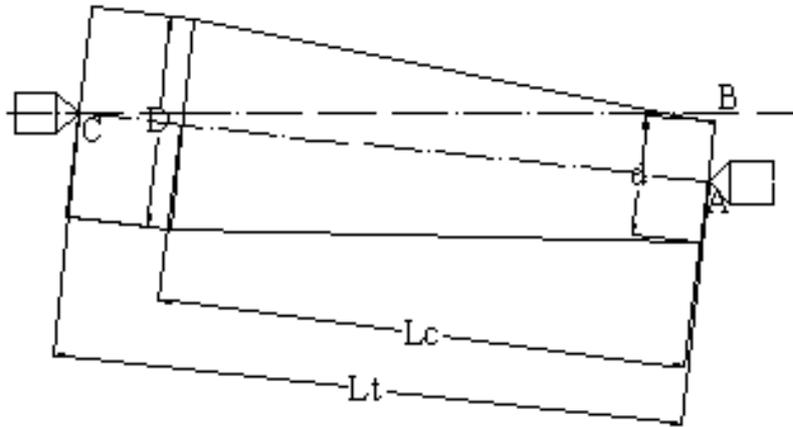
Construcción cónica por desplazamiento del contrapunto
